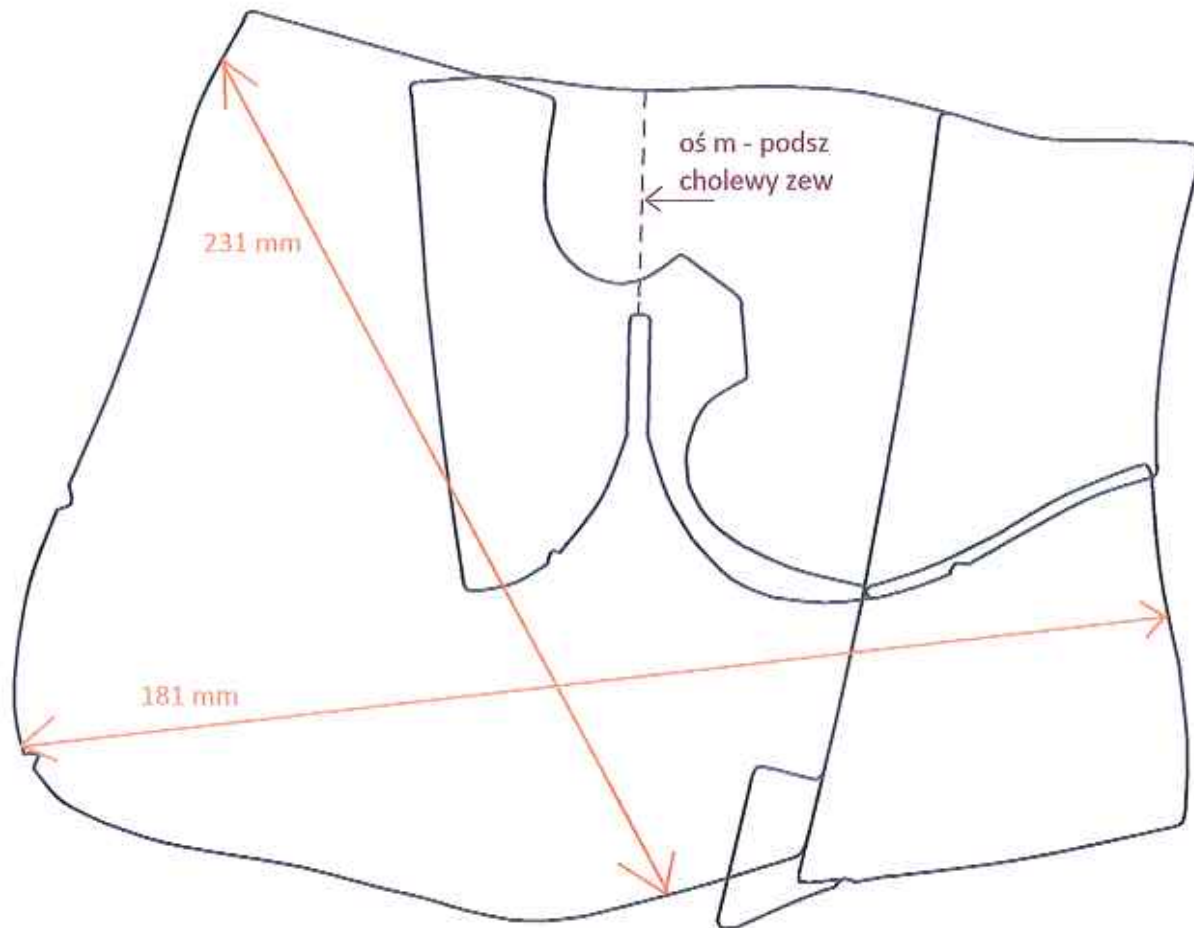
Przykład dla złożenia elementów wierzchnich w rozm.37
